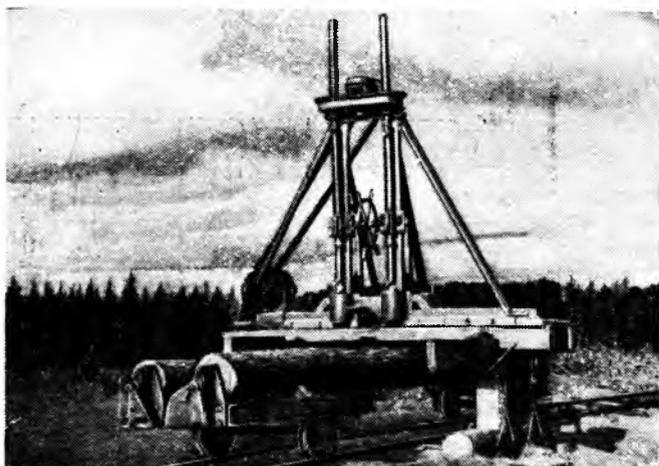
Общий вид сверлильной двухшпиндельной установки
